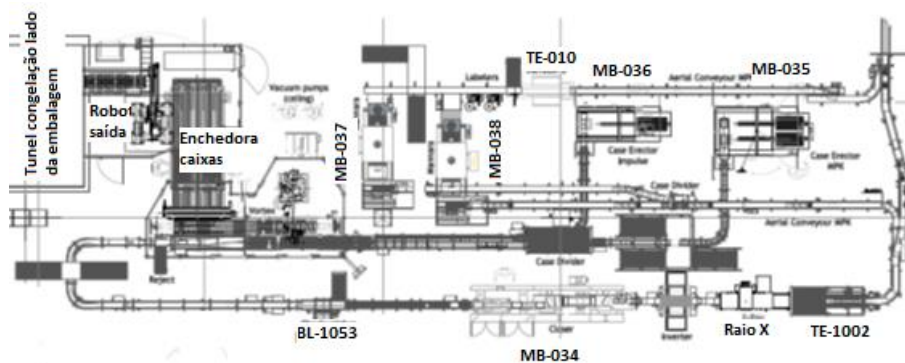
LAY-OUT DA ZONA DE EMBALAMENTO AUTOMÁTICO
